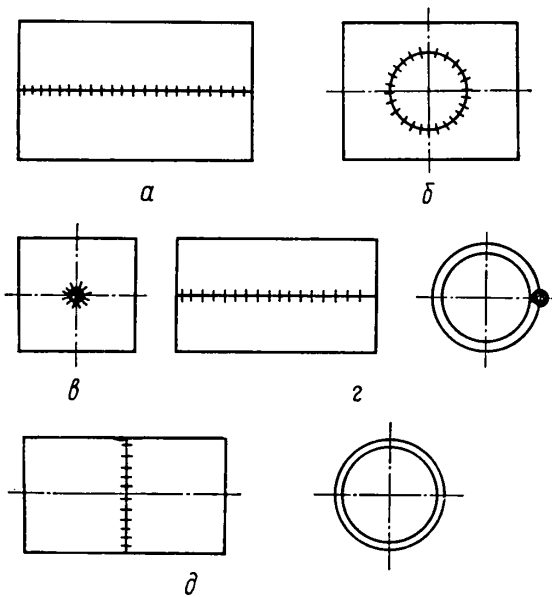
Схемы нанесения сварных швов и виды образцов для испытаний сварных соединений на коррозионное растрескивание:
